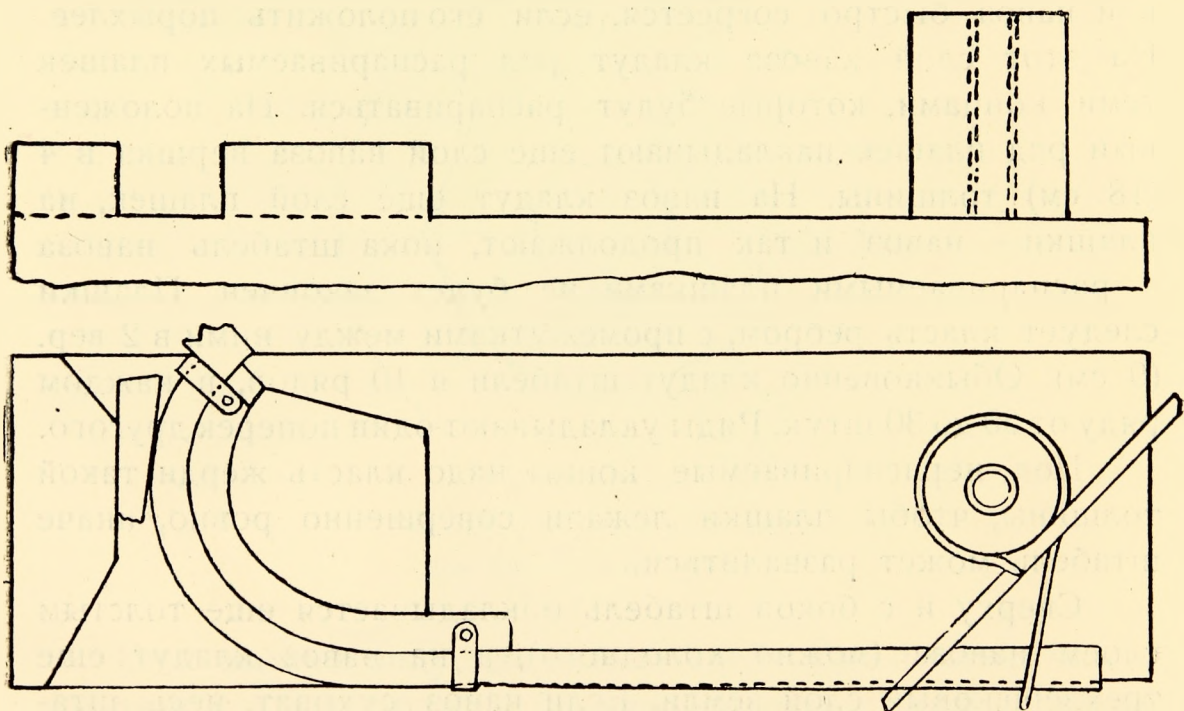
33. Устройство ворота для сгибания полозьев. Сверху—вид гибала сбоку, внизу—вид сверху.
